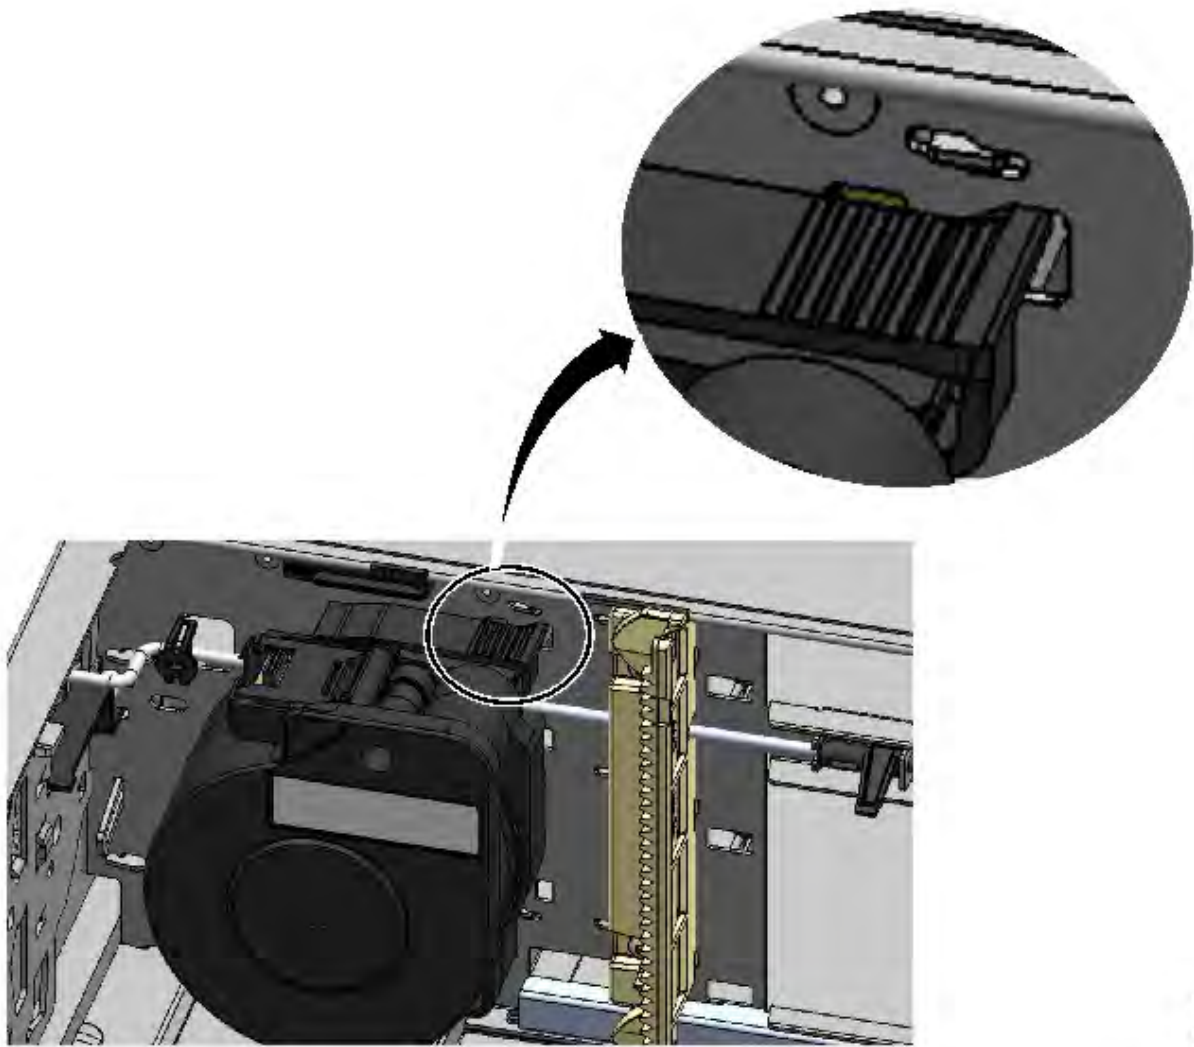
Meccanismo di spooling sbloccato - vista ingrandita
